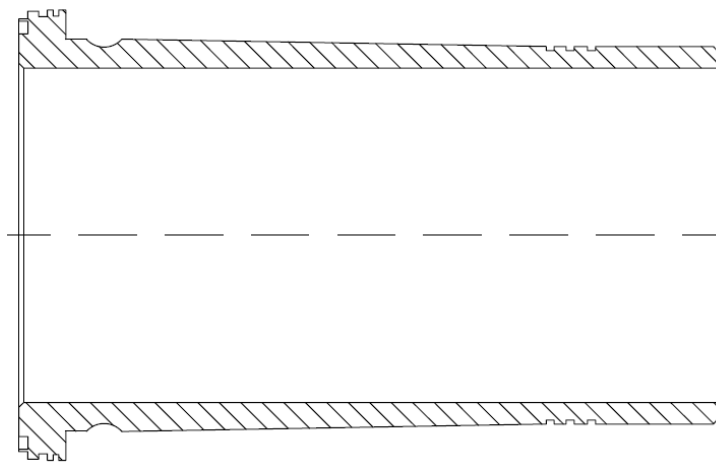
Конструкція втулки робочого циліндра дизеля 6ЧН 28/30
